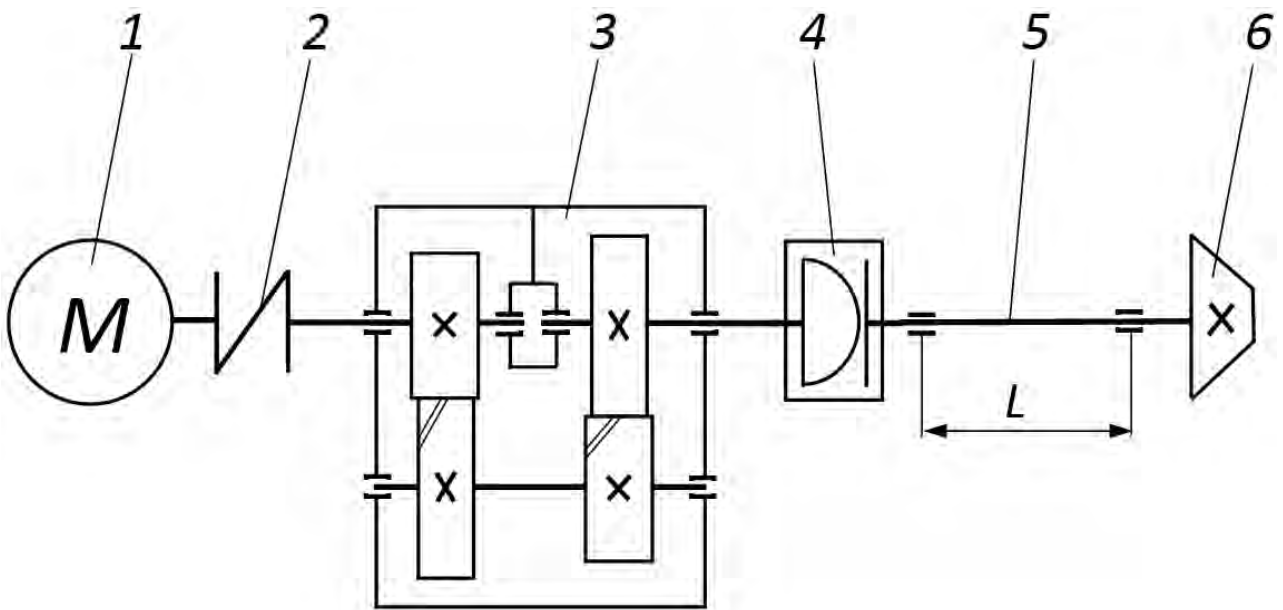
Схема привода поворотного механизма (вид сверху): 1 – асинхронный электродвигатель; 2 – муфта упругая с резиновой звездочкой; 3 – редуктор соосный; 4 – муфта компенсирующая жесткая зубчатая; 5 – приводной вал; 6 – коническая шестерня приводного вала
